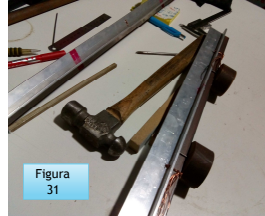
Construcción de equipo colateral para doblado de laminados plásticos
